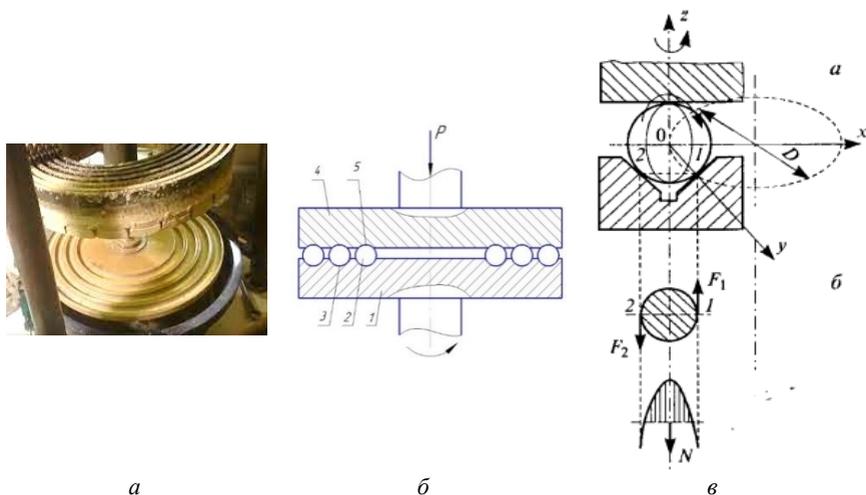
Схема обработки шариков между двумя дисками в кольцевых канавках
